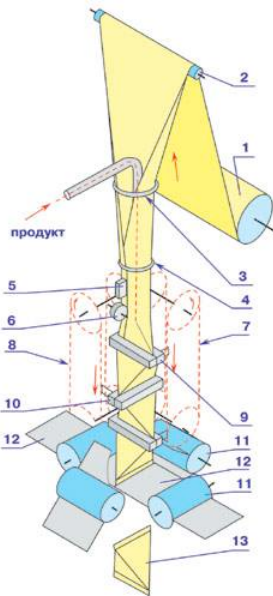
Компонування машини з системою механізмів зварювання і відрізання: 1 – рулон плівки; 2 – натяжний механізм; 3, 4 – формуючий механізм; 5 – механізм поздовжнього зварювання; 9, 10 – губки поперечного зварювання; 11 – ротор; 12 – відрізний механізм; 13 – готовий пакет
